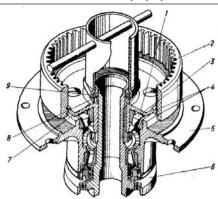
Снятие эпициклического зубчатого колеса, корпуса: 1 — ступица; 2 — колесо зубчатое; 3 — подшипник; 4 — коль-цо стопорное; 5 — картер; 6 — ступица редукторная; 7 — гайка; 8 — шайба; 9 — контргайка
